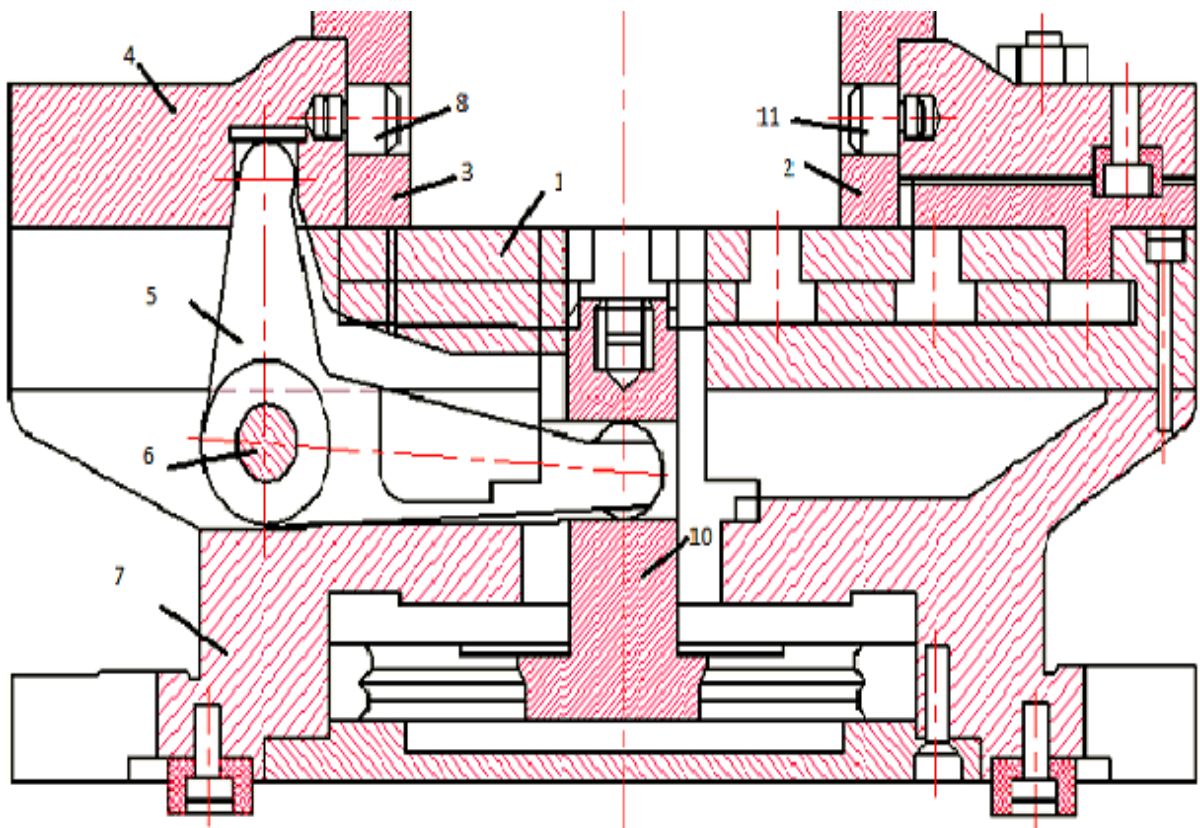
Пристосування для базування корпусних заготовок однієї плоскою зовнішньою поверхнею
